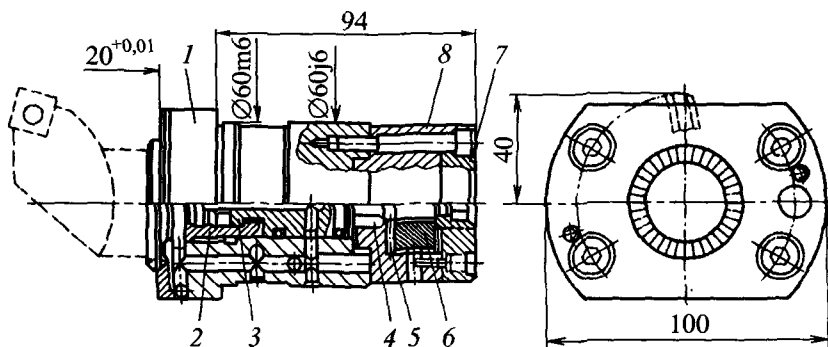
Инструментальный блок с резцовой головкой системы FTS
